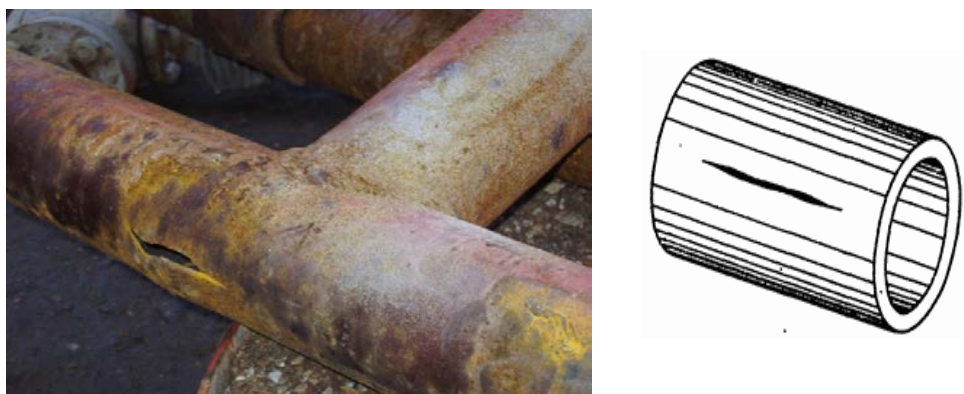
Разрушение цилиндрических трубчатых конструкций
